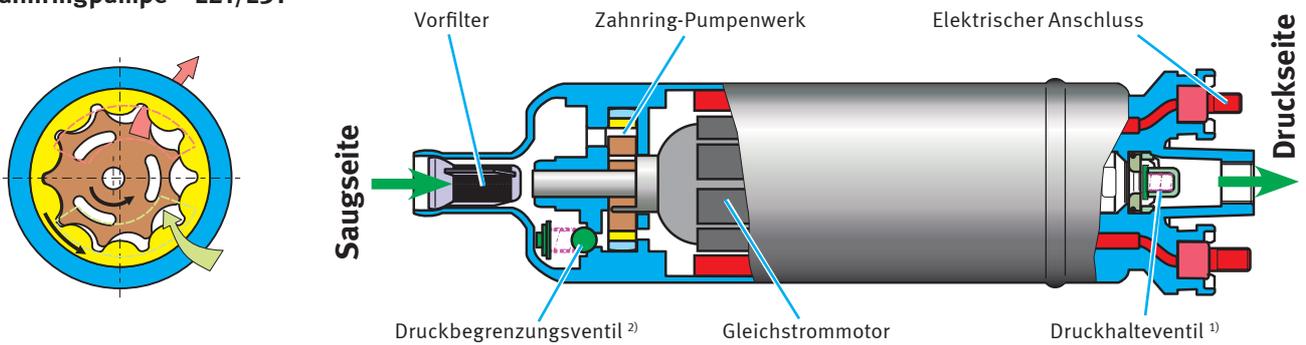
Pumpenprinzip und Schnitt (schematisch) durch eine Zahnringpumpe
